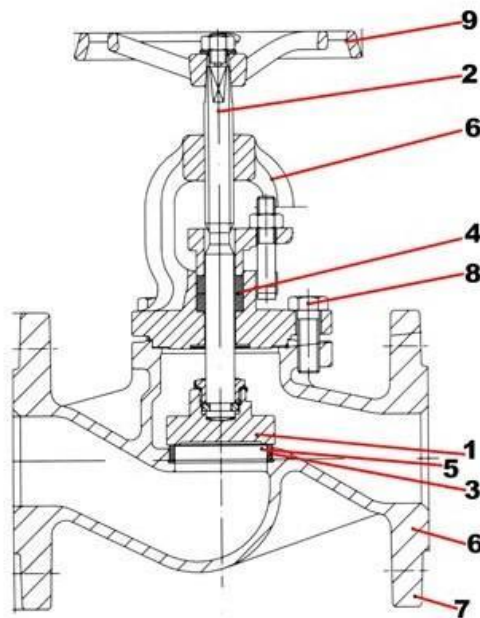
Partes de una válvula hidráulica. Fuente. Zarza (022)
